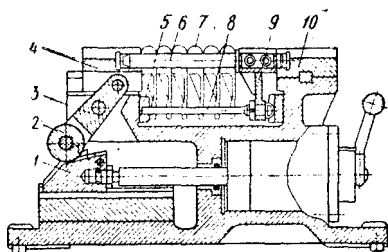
Универсально-наладочное двухрядное приспособление для обработки паза в рычагах
